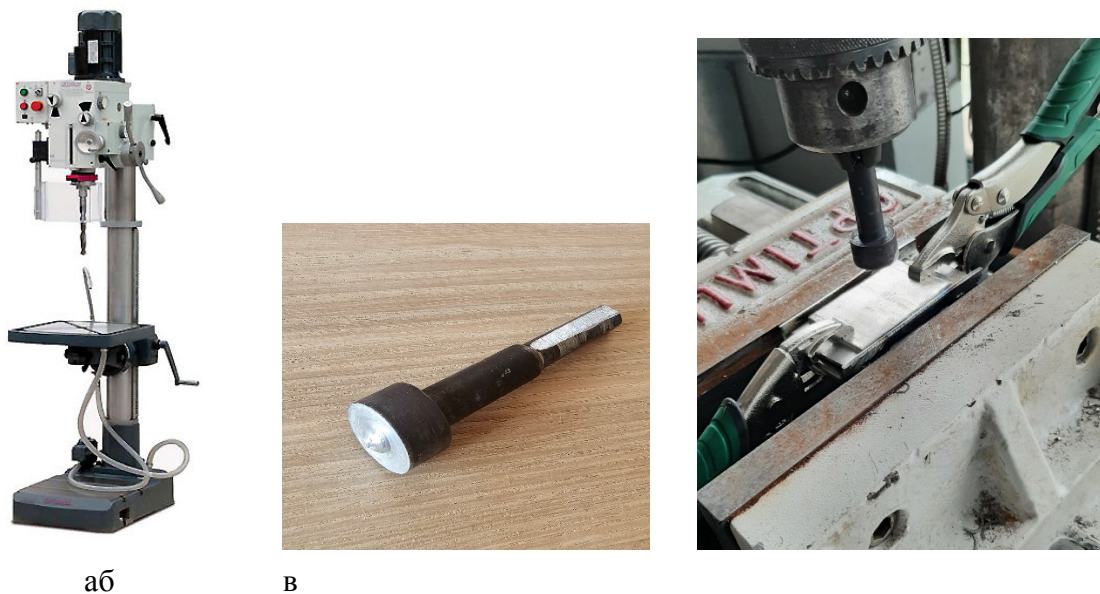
Сверлильный станок ОРТИ В40 РТЕ (а), инструмент для сварки (б),
